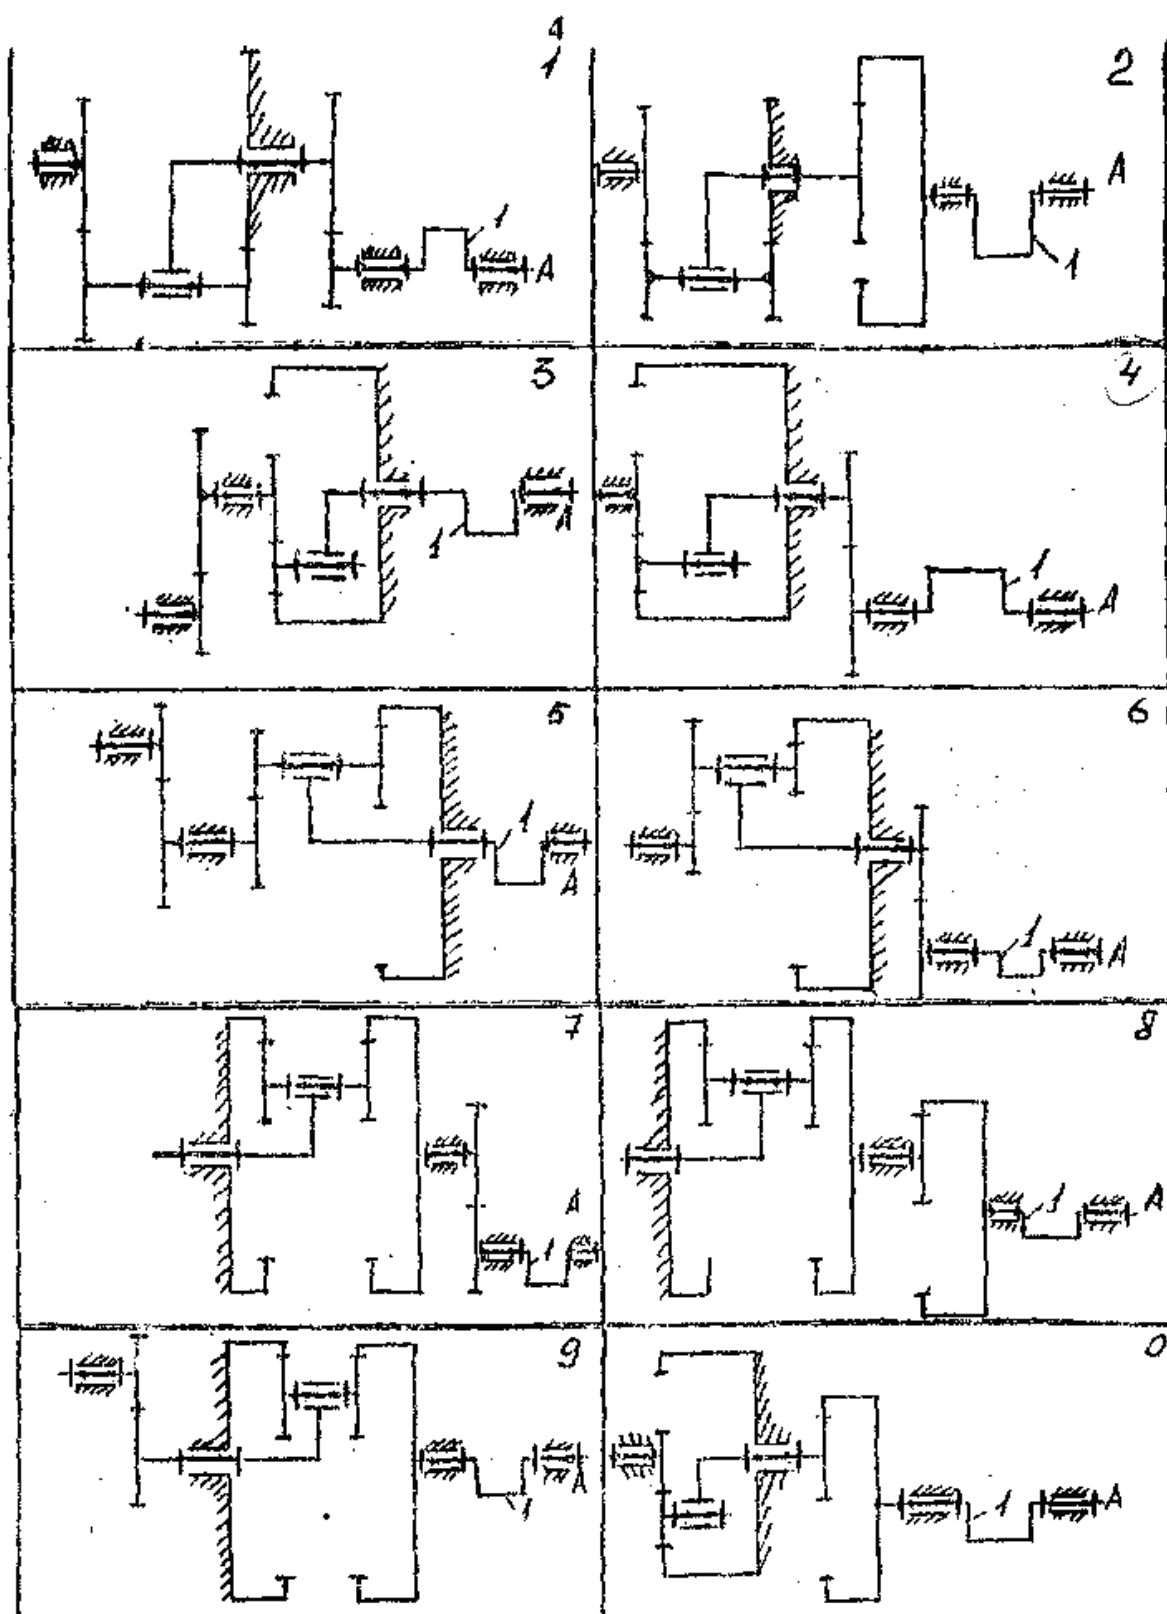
Схемы зубчатых передаточных механизмов (1- кривошип рабочей машины)
